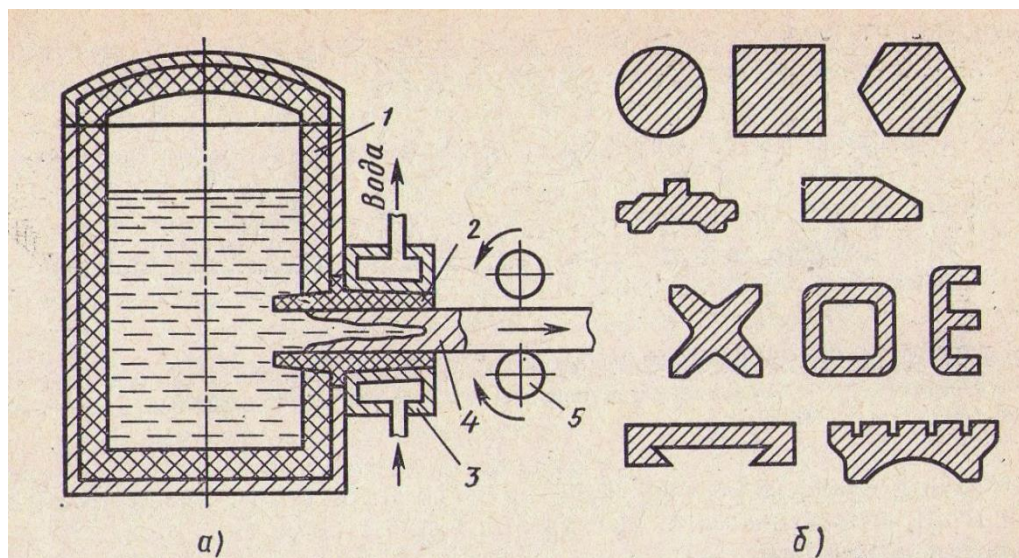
Схема горизонтального непрерывного литья (а) и образцы отливок (б)
